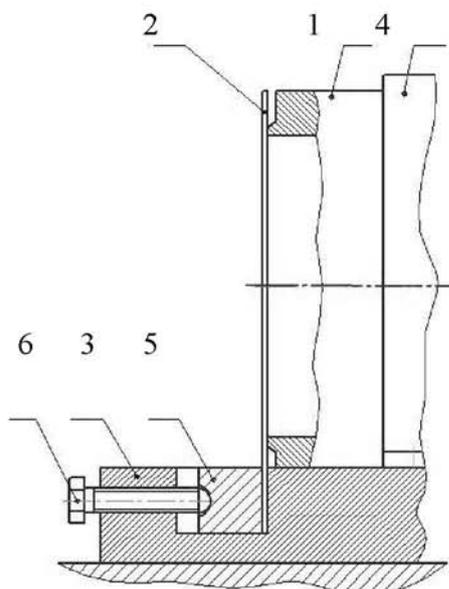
Схема модели клапана: 1 - корпус; 2- рабочая пластина; 3 – основание; 4 – скоба крепежная; 5 - планка опорная; 6 - болт крепежный
